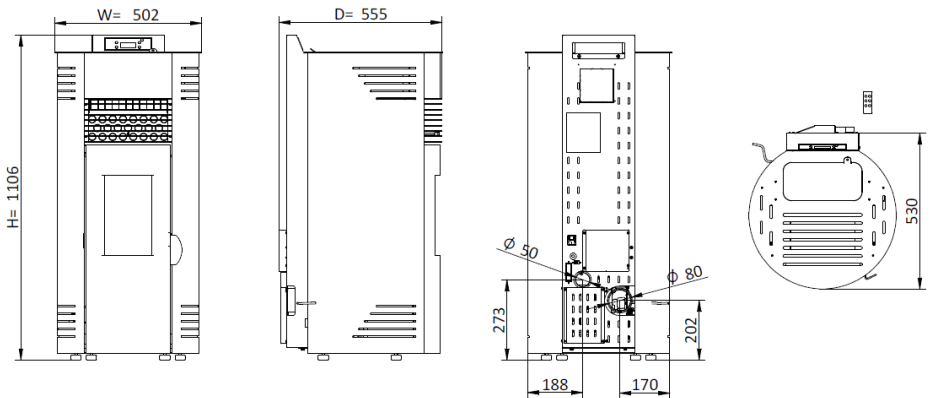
B - Dimensões da salamandra a pellets Indie 8 kW
